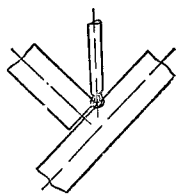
Положение изделия при сварке в лодочку
